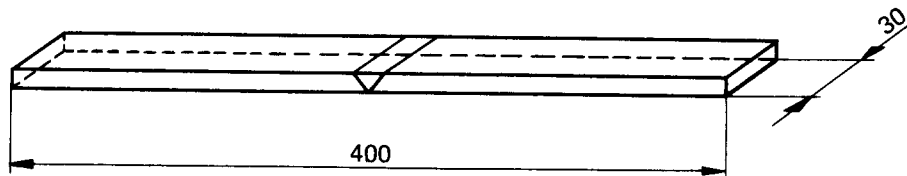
Dimensions de l'éprouvette préparée (acier)
